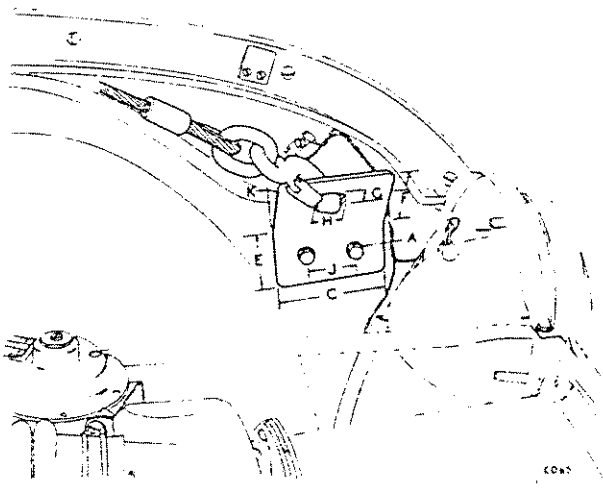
Die an die Befestigungsschrauben des Motorhaubenscharnieres angebrachte Hebeplatte
